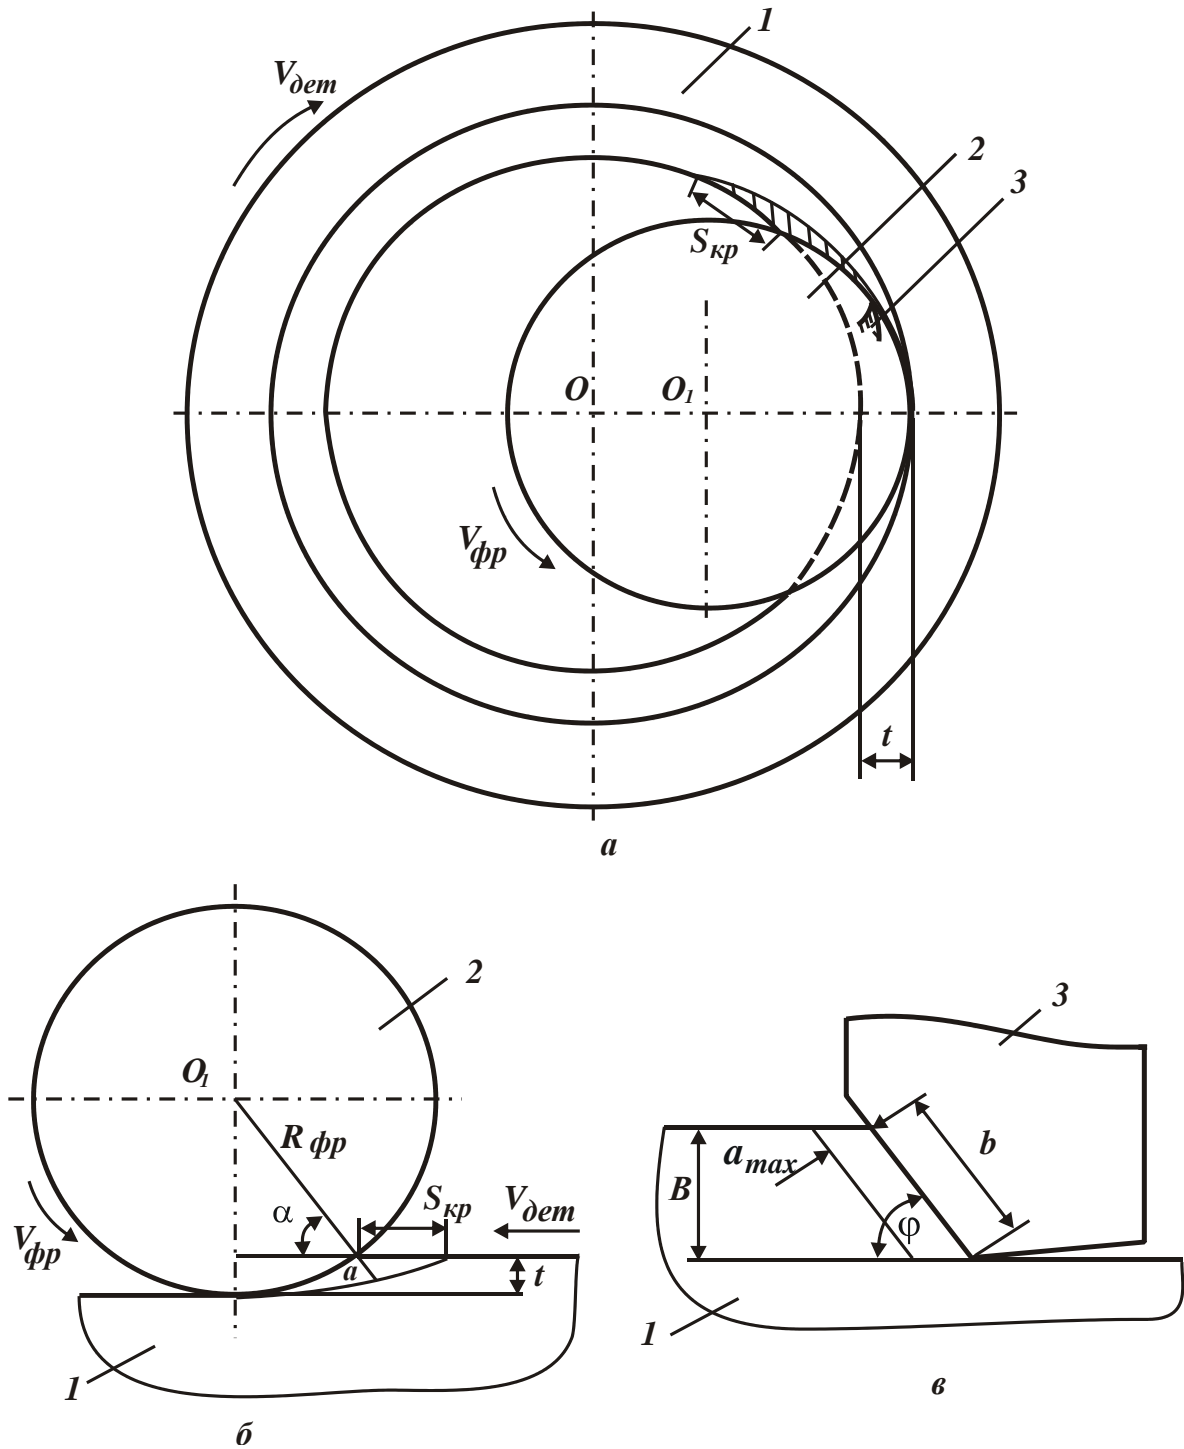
Розрахункові схеми процесу розфрезерування отвору (а, б) і схема різання зубом фрези (в): 1 – деталь (кільце); 2 – фреза; 3 – ріжучий зуб фрези
